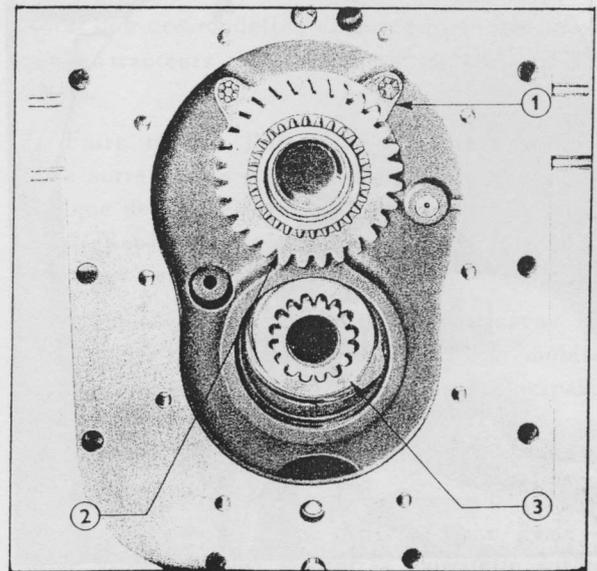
= Plaque d'arrêt d'Arbre de sortie principal
